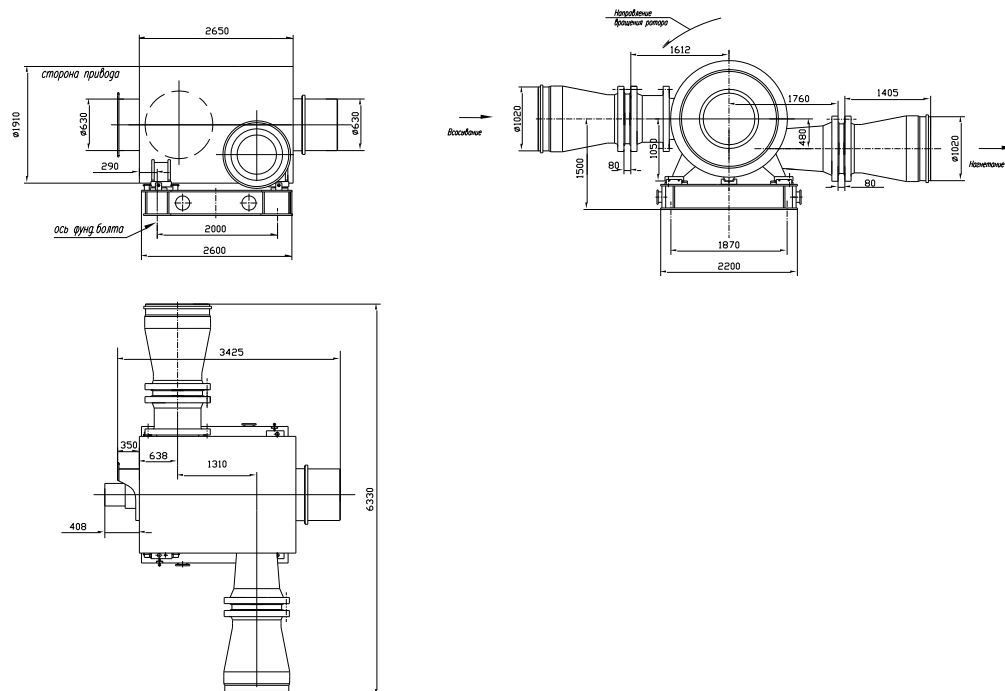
Габаритный чертеж нагнетателя типа 400-21-1С
